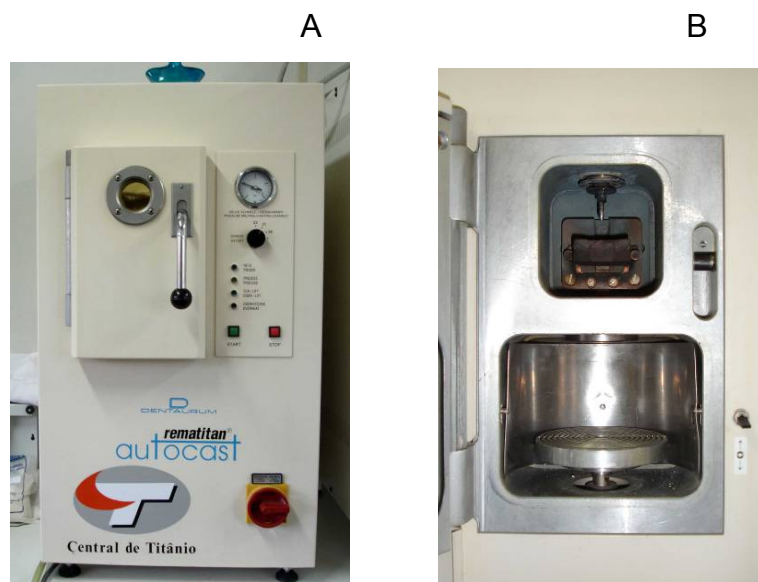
Equipamento utilizado para fundição: a) máquina de fundição (Rematitan® Autocast); b) vista interna da máquina de fundição.
